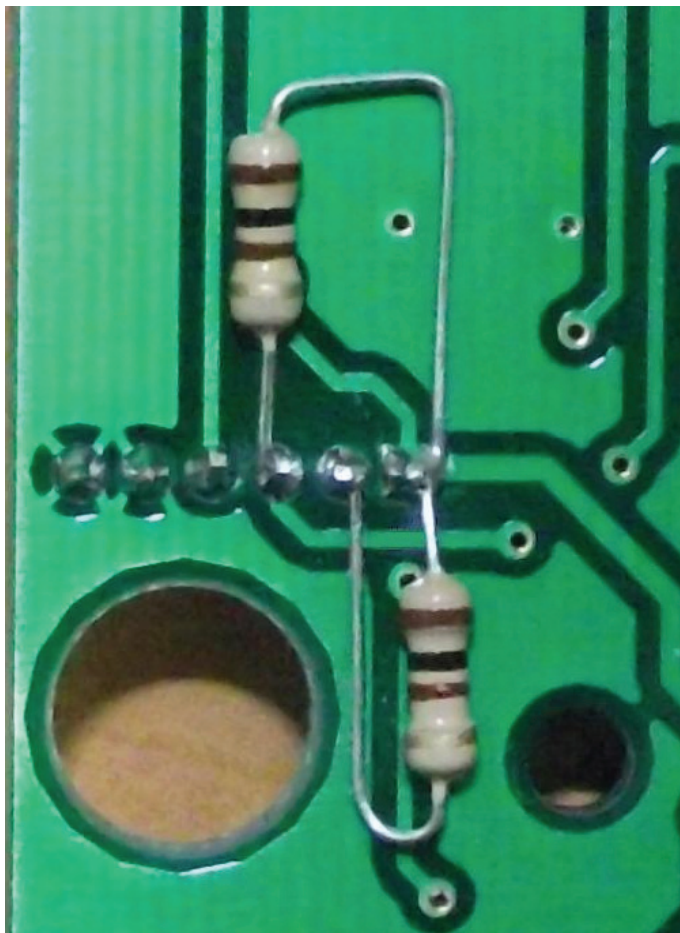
Доработка блока АТ006.01.01 изделия ККМ/ПД FPrint-03(К).
